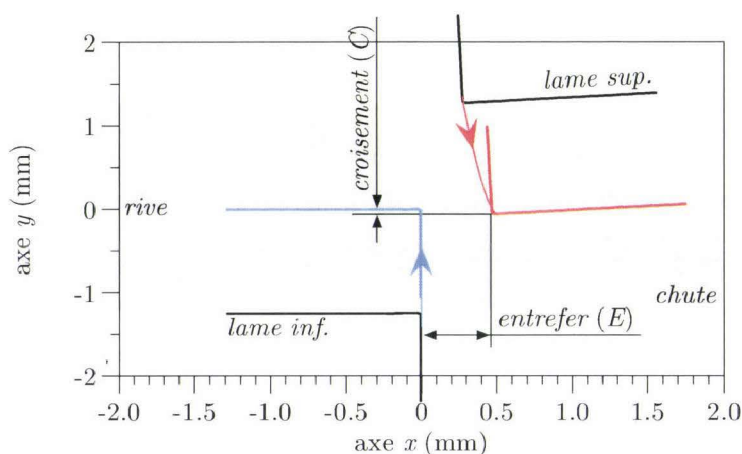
Trajectoire des lames de la cisaille dans le plan de modélisation (plan xy).
